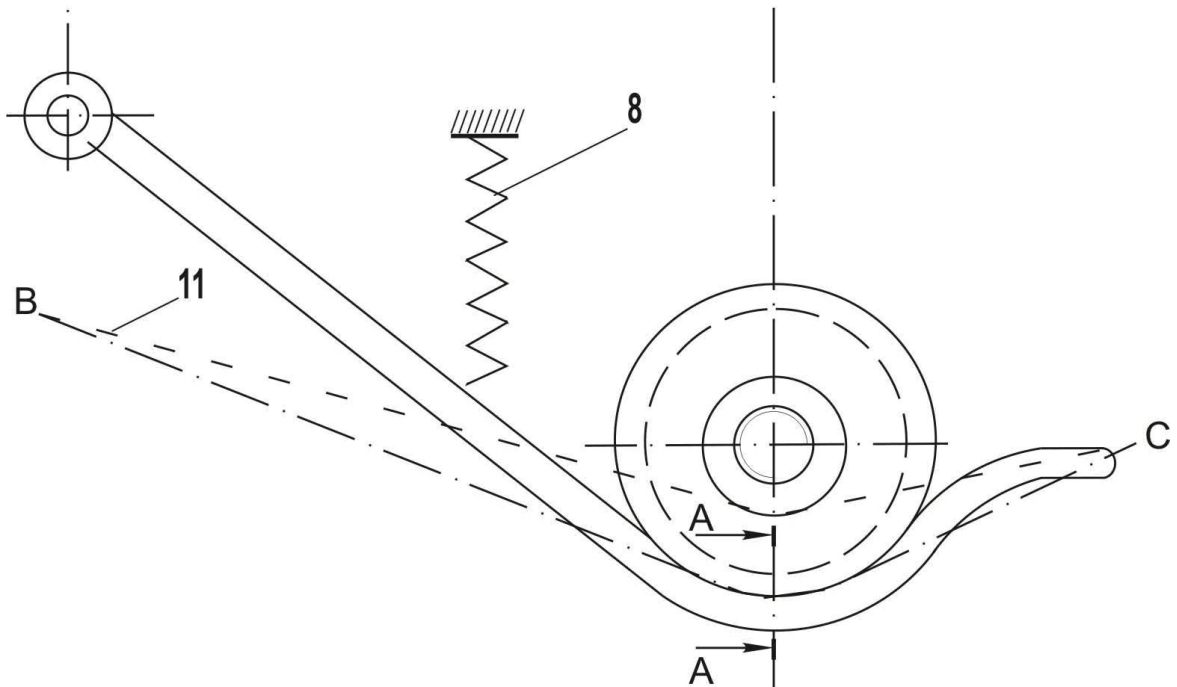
Нитконатягувальний пристрій (вид зверху)
